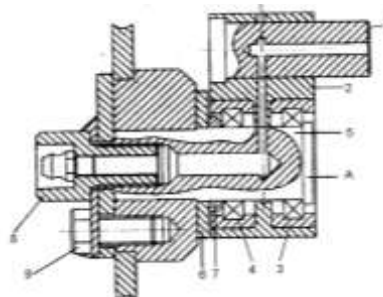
Опорный узел коромысла-бойка конструкции Шаршеева Ф.
